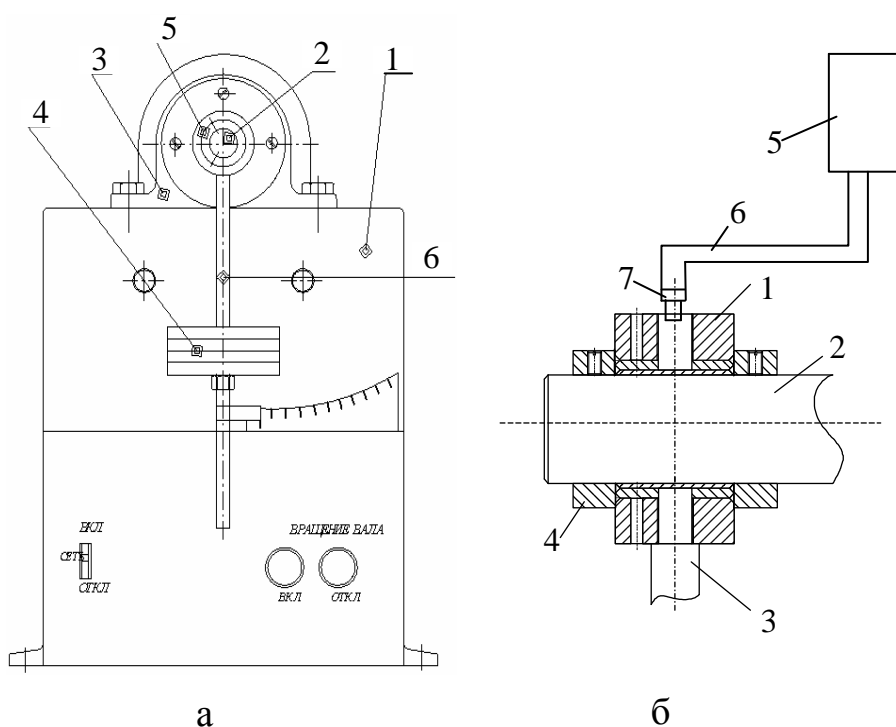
а) Машина трения ДМ-28, б) узел трения, где 1 – корпус, 2 – вал, 3 – стержень, 4 – кольцо, 5 – емкость со смазкой; 6 – соединительная трубка; 7 – герметизирующий наконечник.
